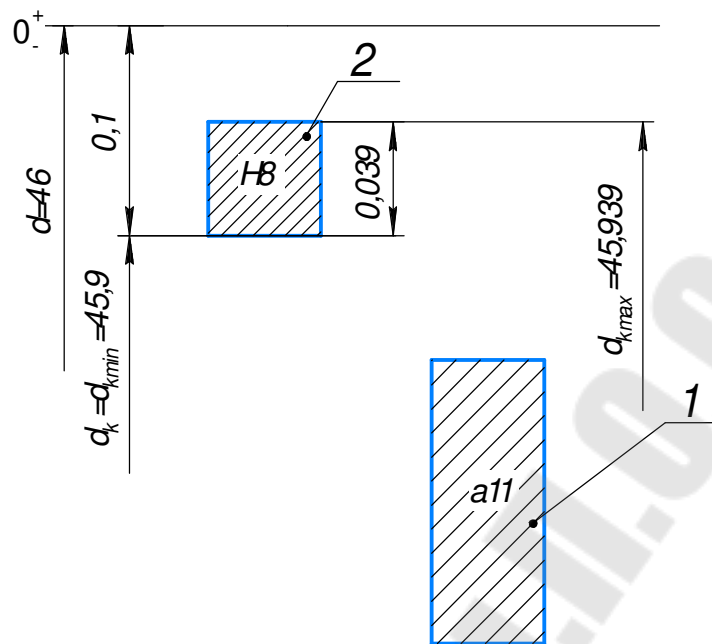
Схема расположения полей допусков, нецентрирующего диаметра d калибра–кольца: 1 – поле допуска размера d вала; 2 – поле допуска d_k на изготовление калибра-кольца.
